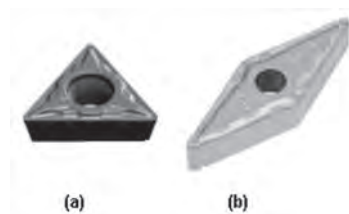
(a) Inserto de carburo de tungsteno y (b) Inserto de cermet para torno CNC.
